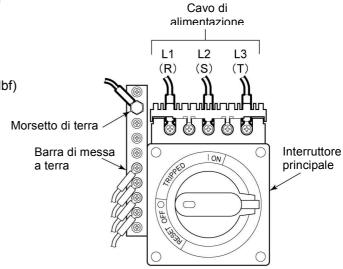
Collegamento del cavo di alimentazione e morsetto di terra
